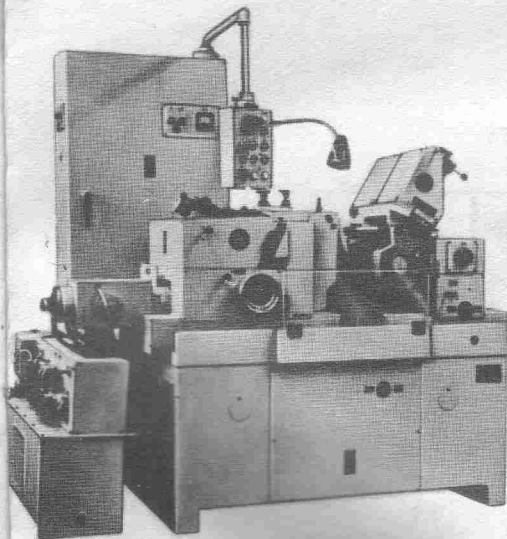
Круглошлифовальный бесцентровый станок ЗМ182
